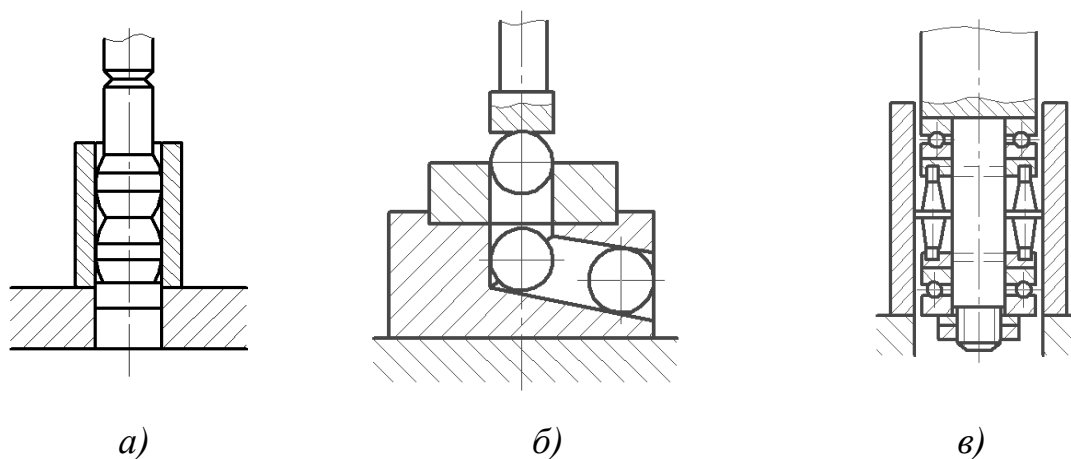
Схеми обробки отворів без зняття стружки:
